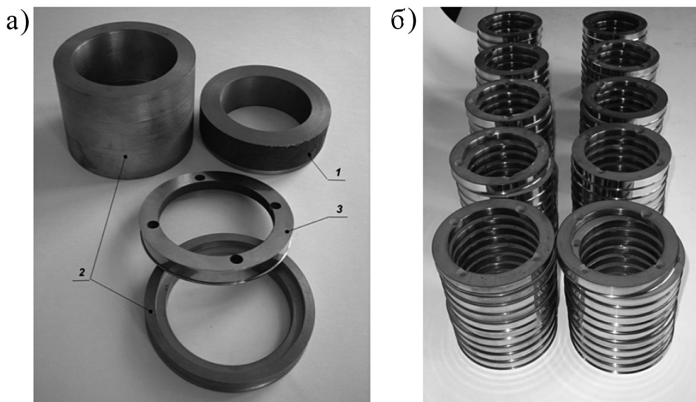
Обработанная отливка (1), заготовки (2) и деталь «диск тормозной» (3) из БВХЧ (а) и опытно-промышленная партия дисков тормозных (б)
